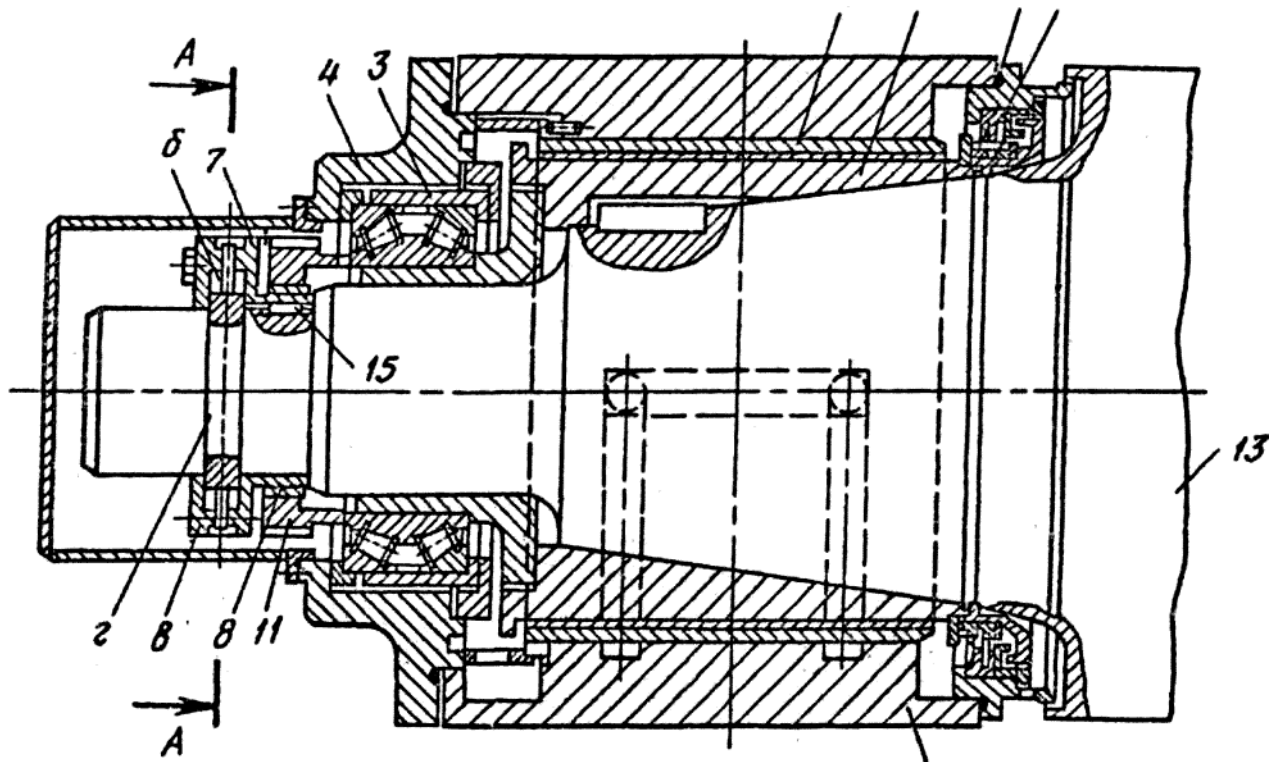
Підшипникова опора, поздовжній розріз
